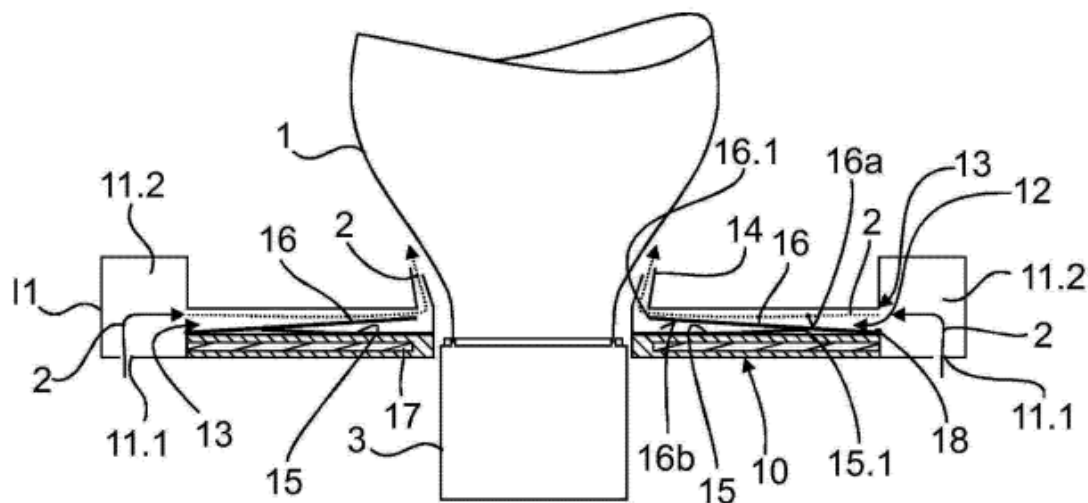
Схематичний вид пристрою для охолодження плівки:
